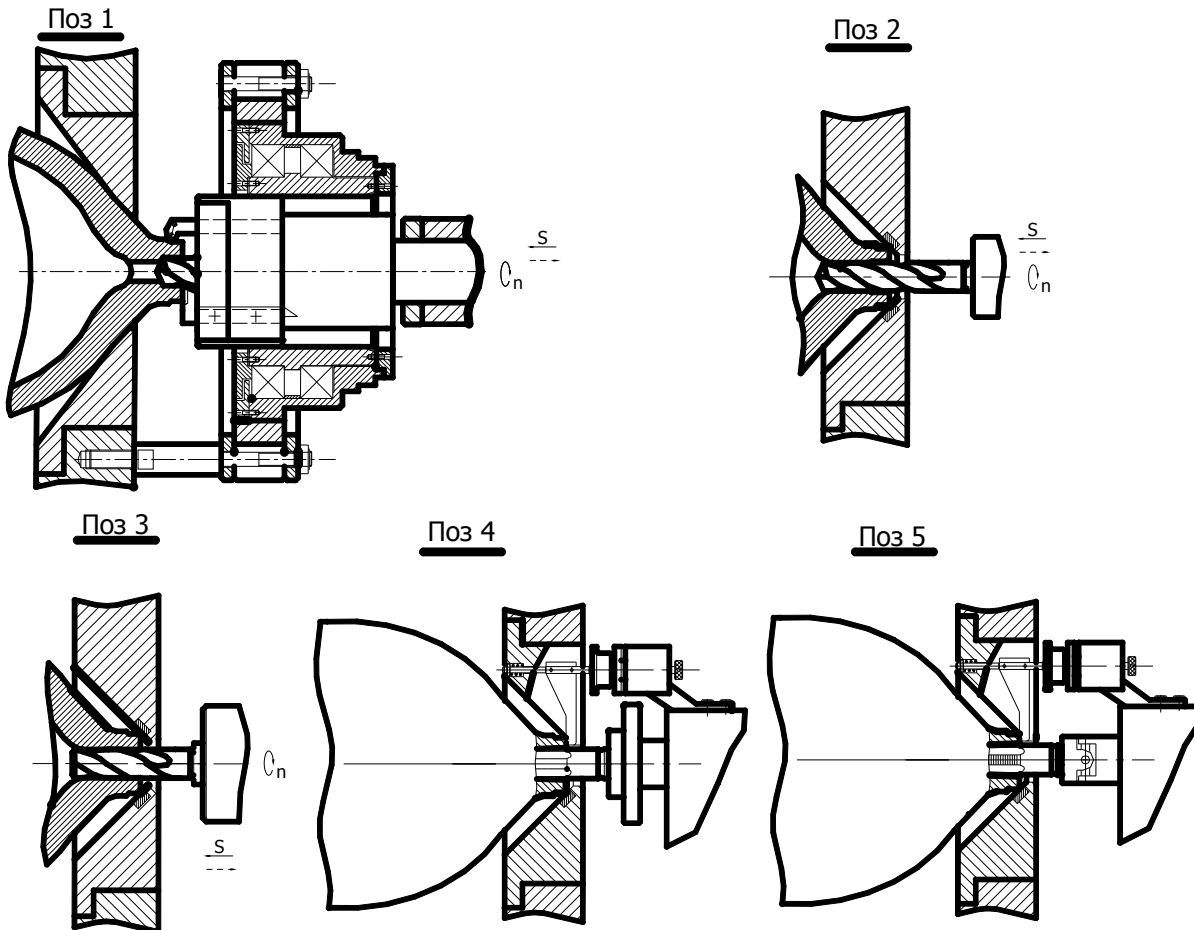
Розроблений технологічний процес механічної обробки різьбового отвору в горловині балона.
